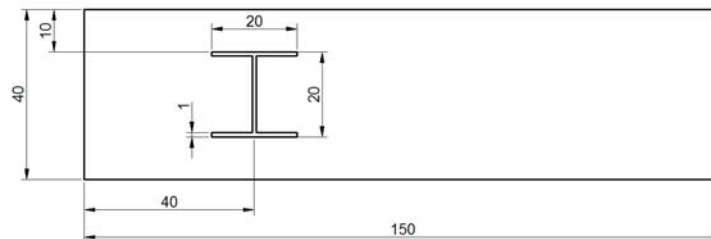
Схема деталі для зразка з Н-подібним з'єднанням
